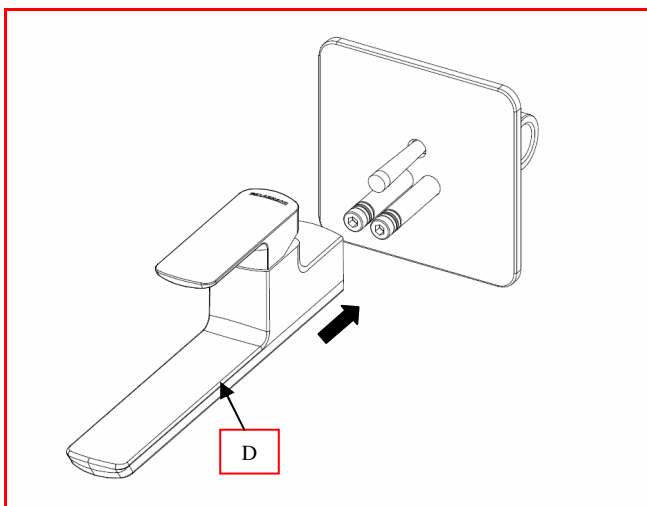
MONTAGGIO GRUPPO RUBINETTO
